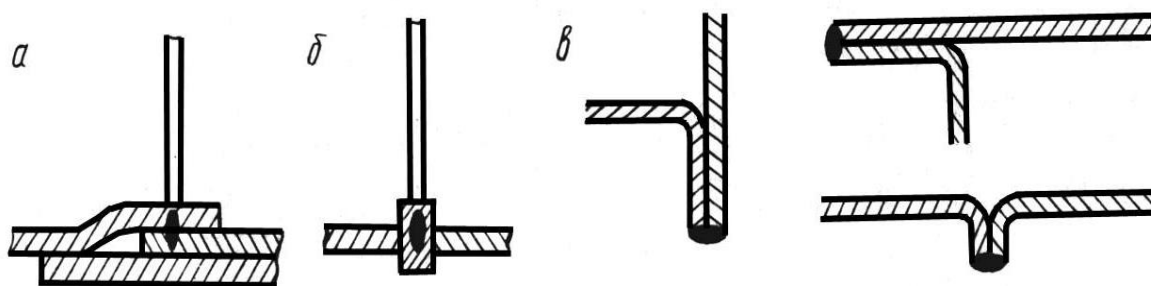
Техника сварки тонколистовой стали
